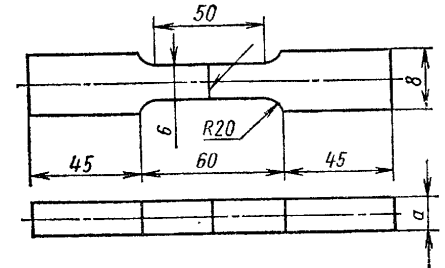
Образец для испытания сварного соединения на ударный разрыв
